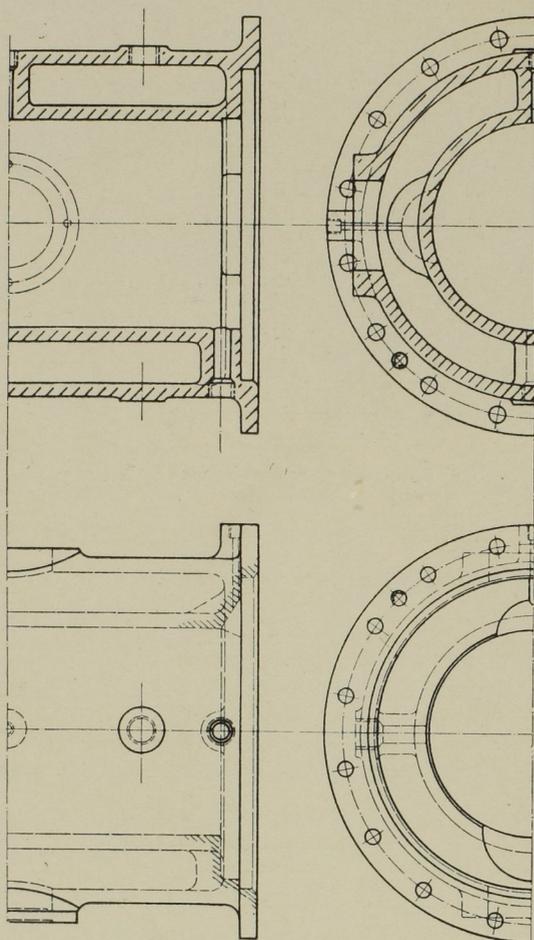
Hochdruck-Kompressorzylinder. Massst. 1:12.
